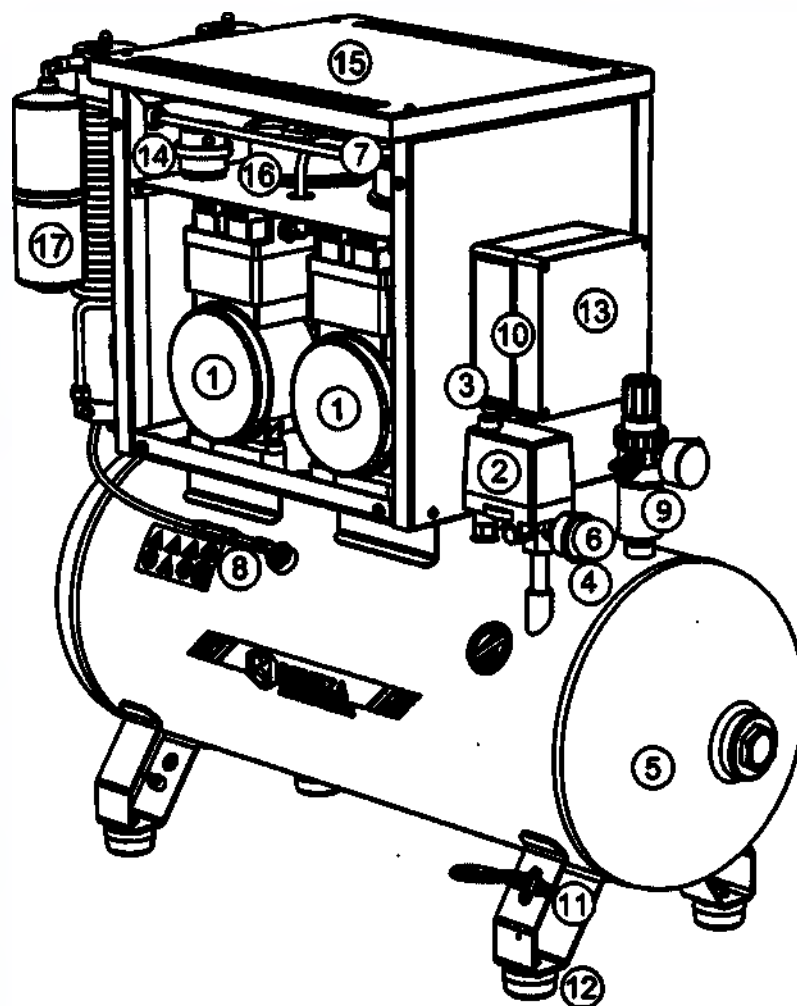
Общий вид компрессора KM-100.OLD15TKД и KM-100.OLD20TKД
